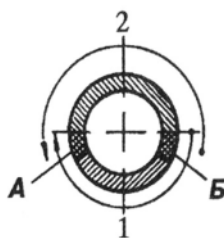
Последовательность сварки неповоротного стыка труб диаметром до 150 мм
